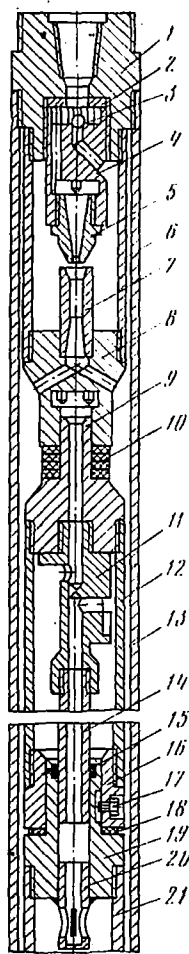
Двойной эжекторный колонковый снаряд ЭКС-Ш со шламособорителем.
